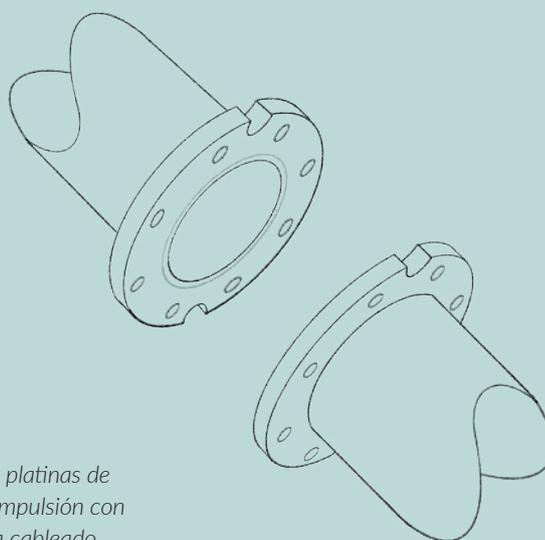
Detalle de las platinas de unión de una tubería de impulsión con dos muescas a 180° para cableado.
